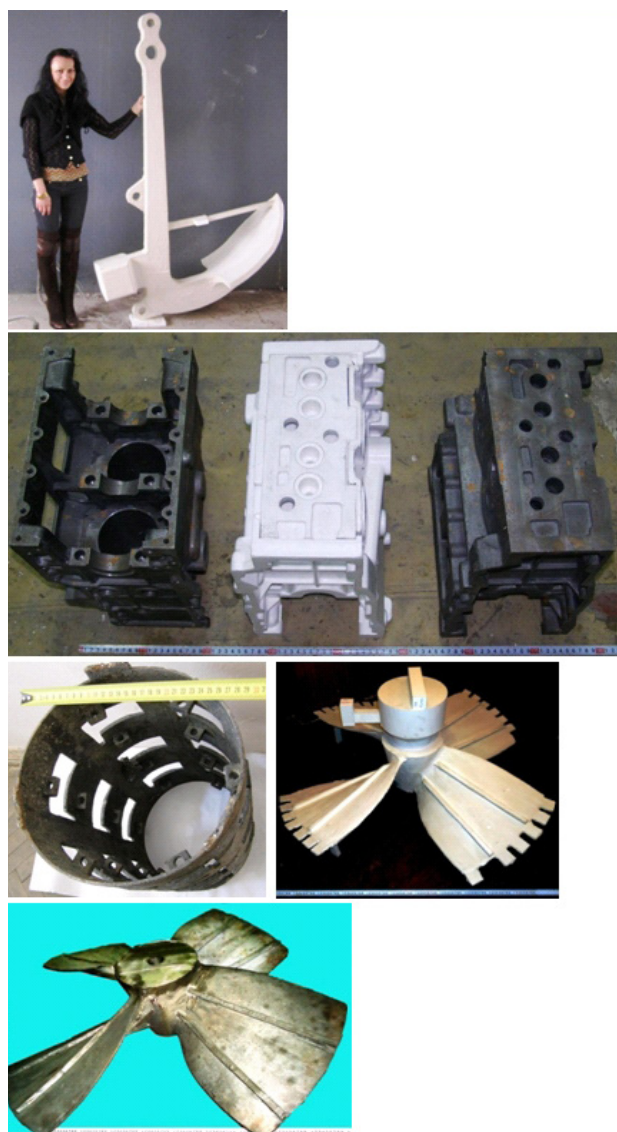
Модель якоря, отливки и модель 2-цилиндрового двигателя, корпус касетного изделия, модель винта и его отливка из нержавеющей стали.
